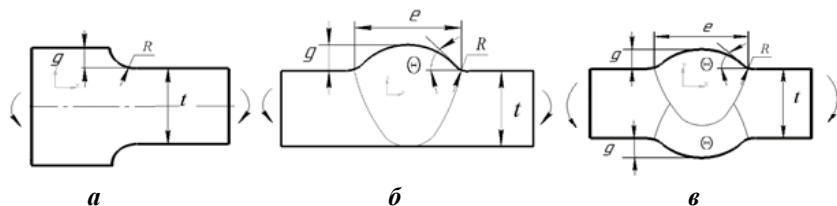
Схема прерывистой связи и сварного соединения:
